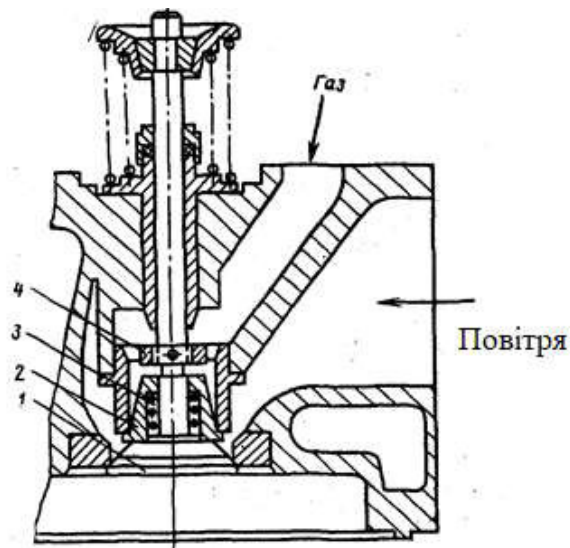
Клапан - змішувач: 1 – впускний клапан; 2 – газовий клапан; 3 – пружина; 4 – стопорне кільце
